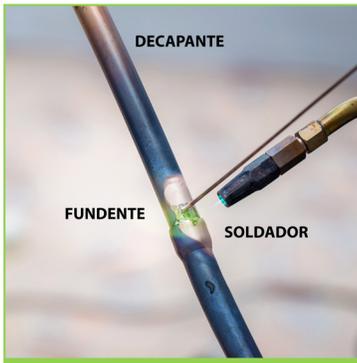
Imagen de una soldadura fuerte de cobre y sus componentes.
